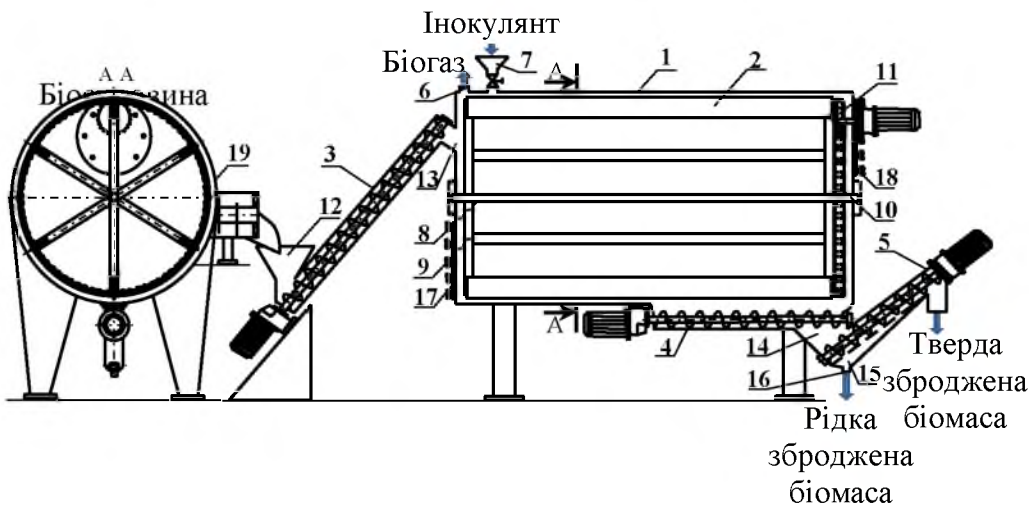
Біогазовий реактор: 1 – горизонтальний циліндричний корпус; 2 – лопатки; 3, 4, 5 – гвинтові транспортери; 6 – патрубок для відводу біогазу; 7 – пристрій для інокуляції біомаси; 8 – центральний горизонтальний вал; 9 – обертово-лопатевого механізму; 10 – кільцевий ланцюг; 11 – привідна зірочка; 12 – бункер для завантаження біомаси; 13 – патрубок; 14 – камера; 15 – камера збору рідкої збродженої фракції; 16 – патрубок для видалення рідкої біомаси; 17, 18 – люки; 19 – подрібнювач біосировини.
